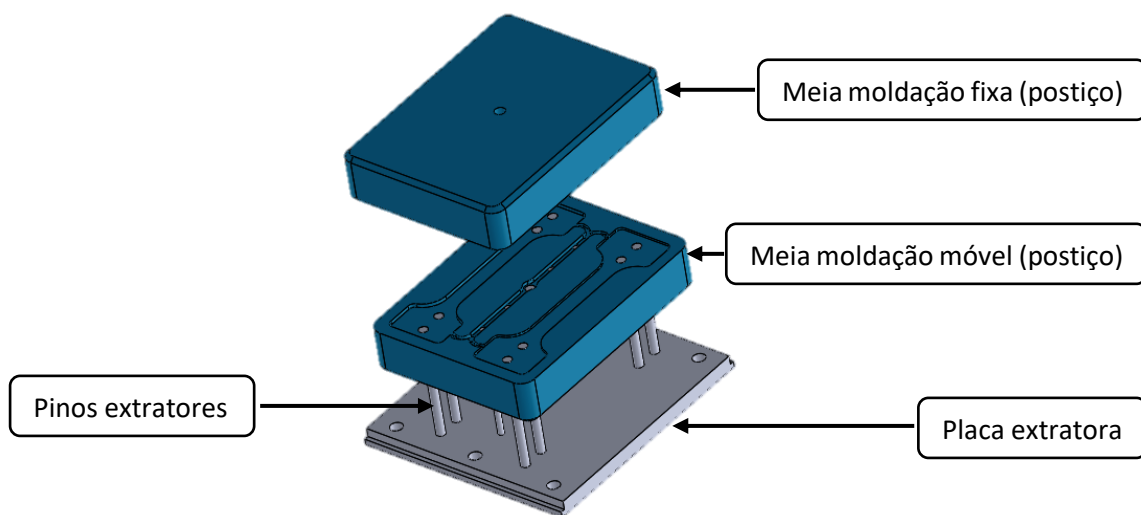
Desenho tridimensional das moldações e placas extratoras da moldação dos provetes
